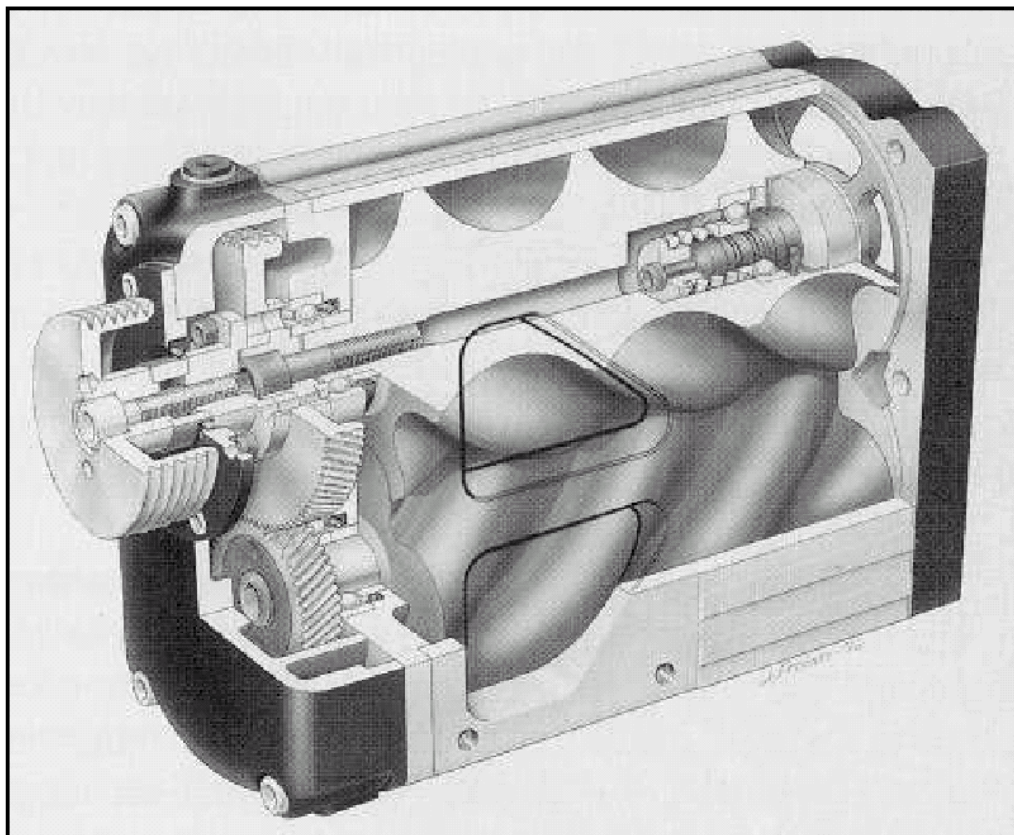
Schnittbild eines Opcon-Autorotor Schraubenladers [69]
